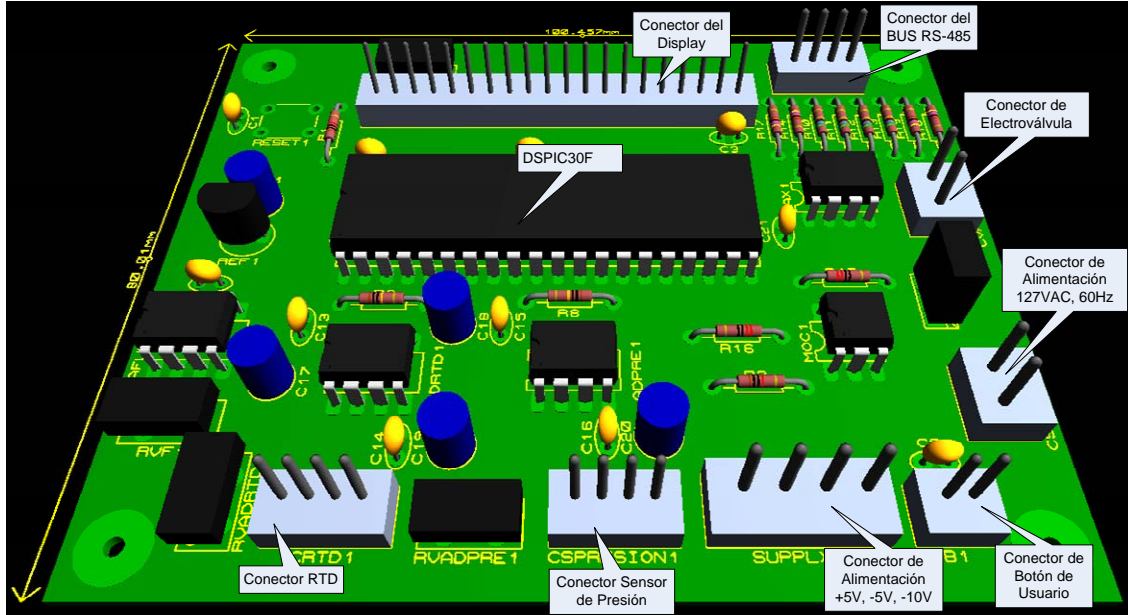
Aspecto 3D de la PCB de la TEC.
